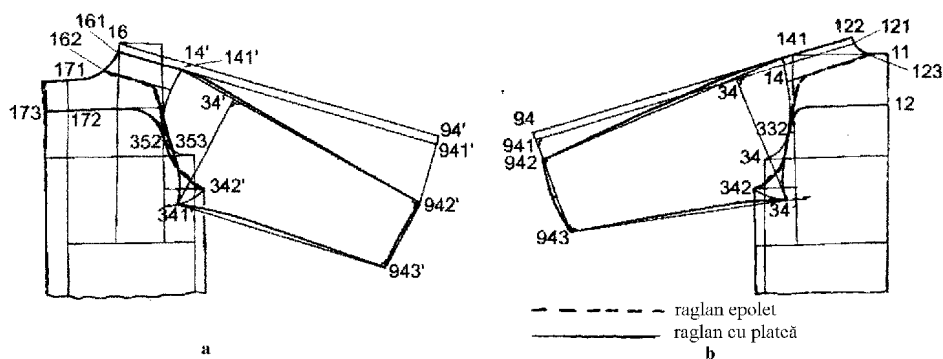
Construcția tiparelor pentru raglanul „epolet” și „cu placă”.
